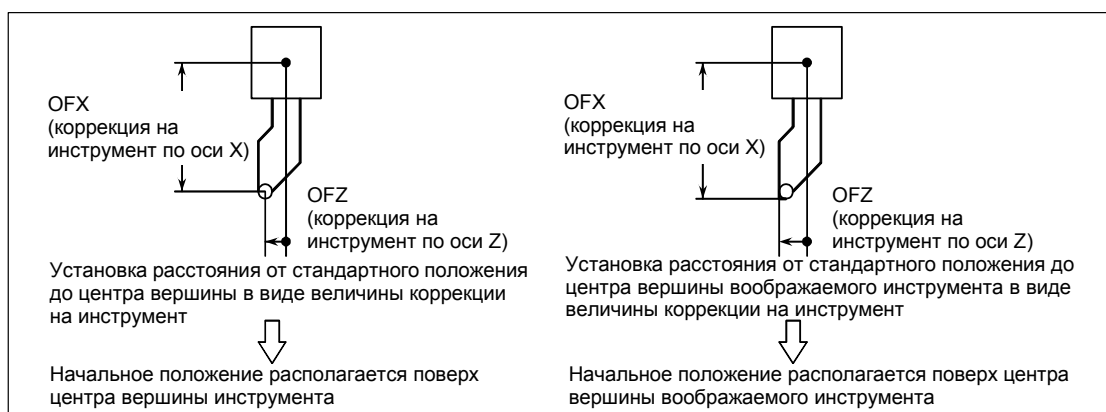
(b) Величина коррекции на инструмент, когда центр револьверной головки располагается поверх начальной точки
